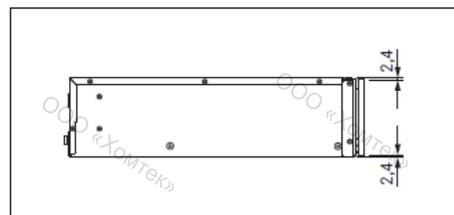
Размеры прибора, модель MS140, вид сбоку
